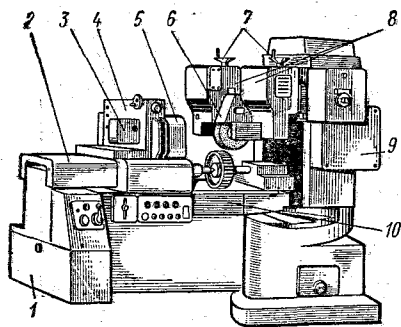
Универсальный зубошлифовальный станок мод. 5851
